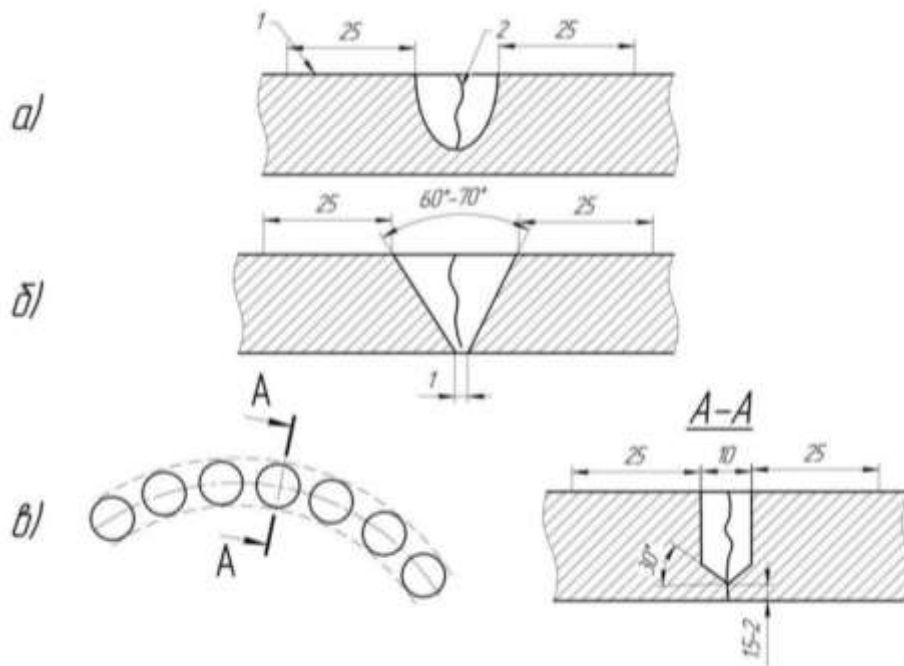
Форми та способи розробки тріщин під зварювання
